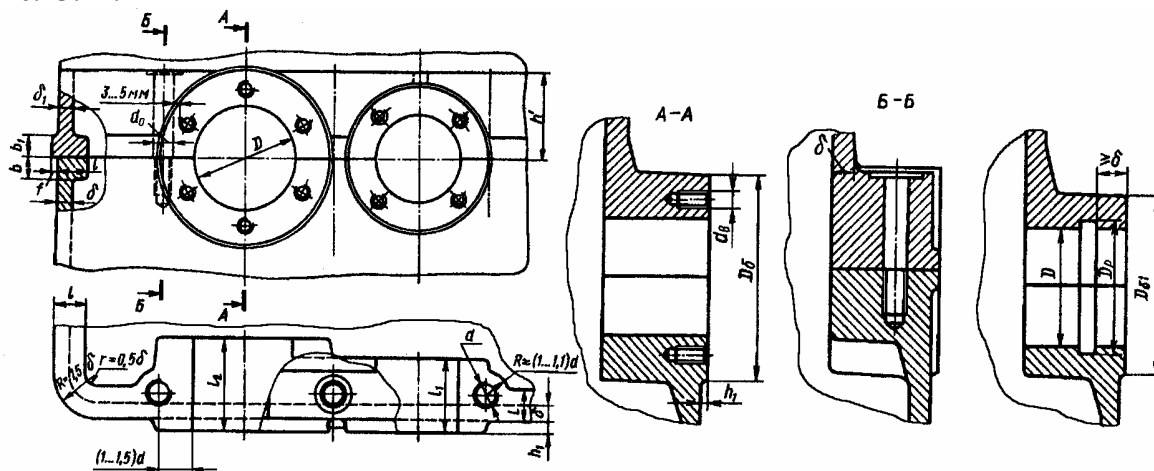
Расположение болтов крепления в плоскости разъема редуктора
